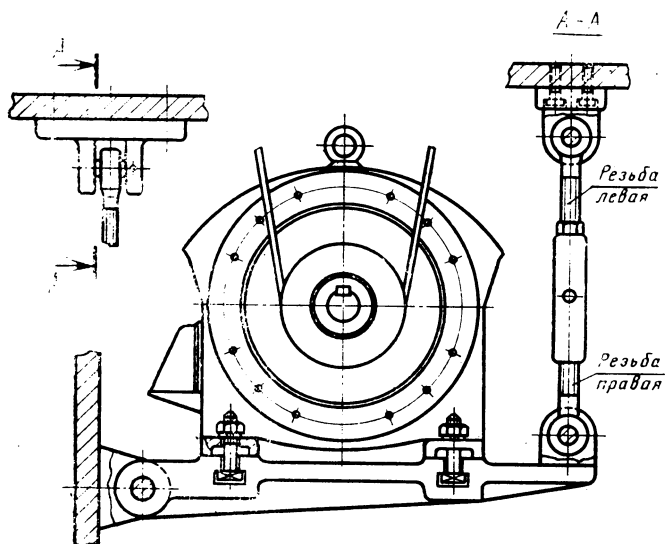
Натяжное устройство с качающейся плитой и резьбовой тягой
